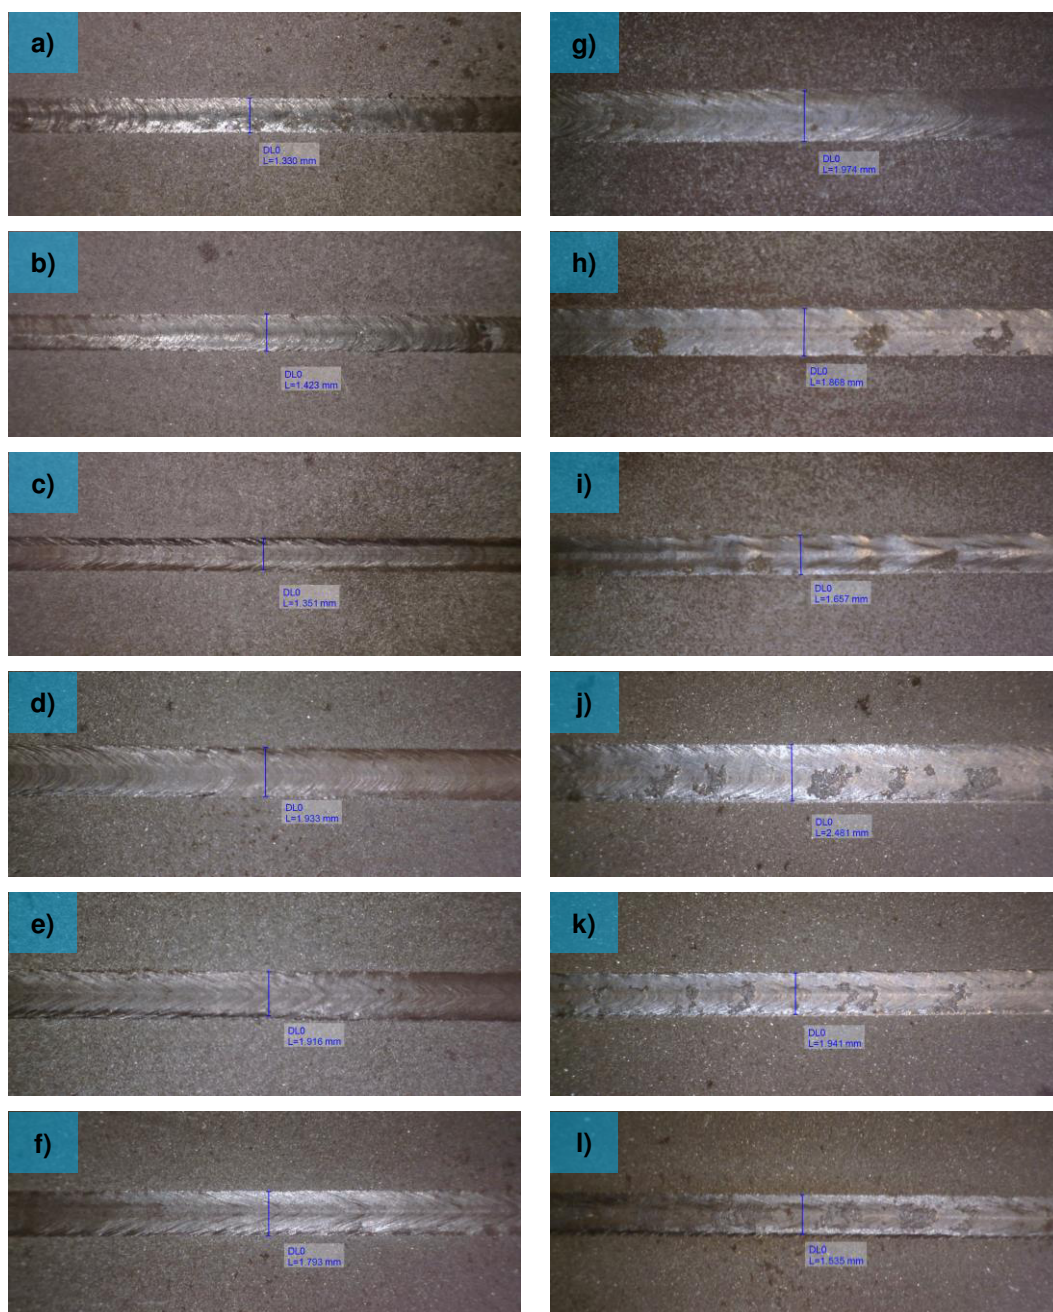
Cordones de soldadura del acero HSLA.
